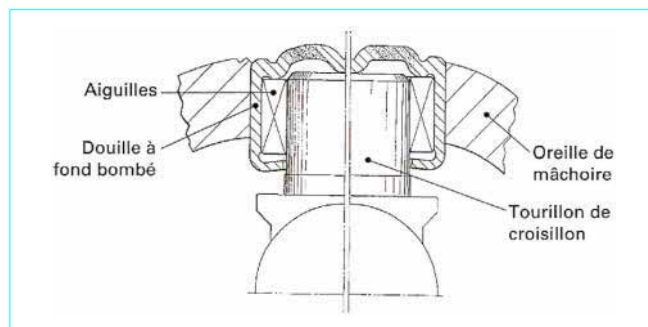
Centrage d'un joint de cardan avec douilles à aiguilles
